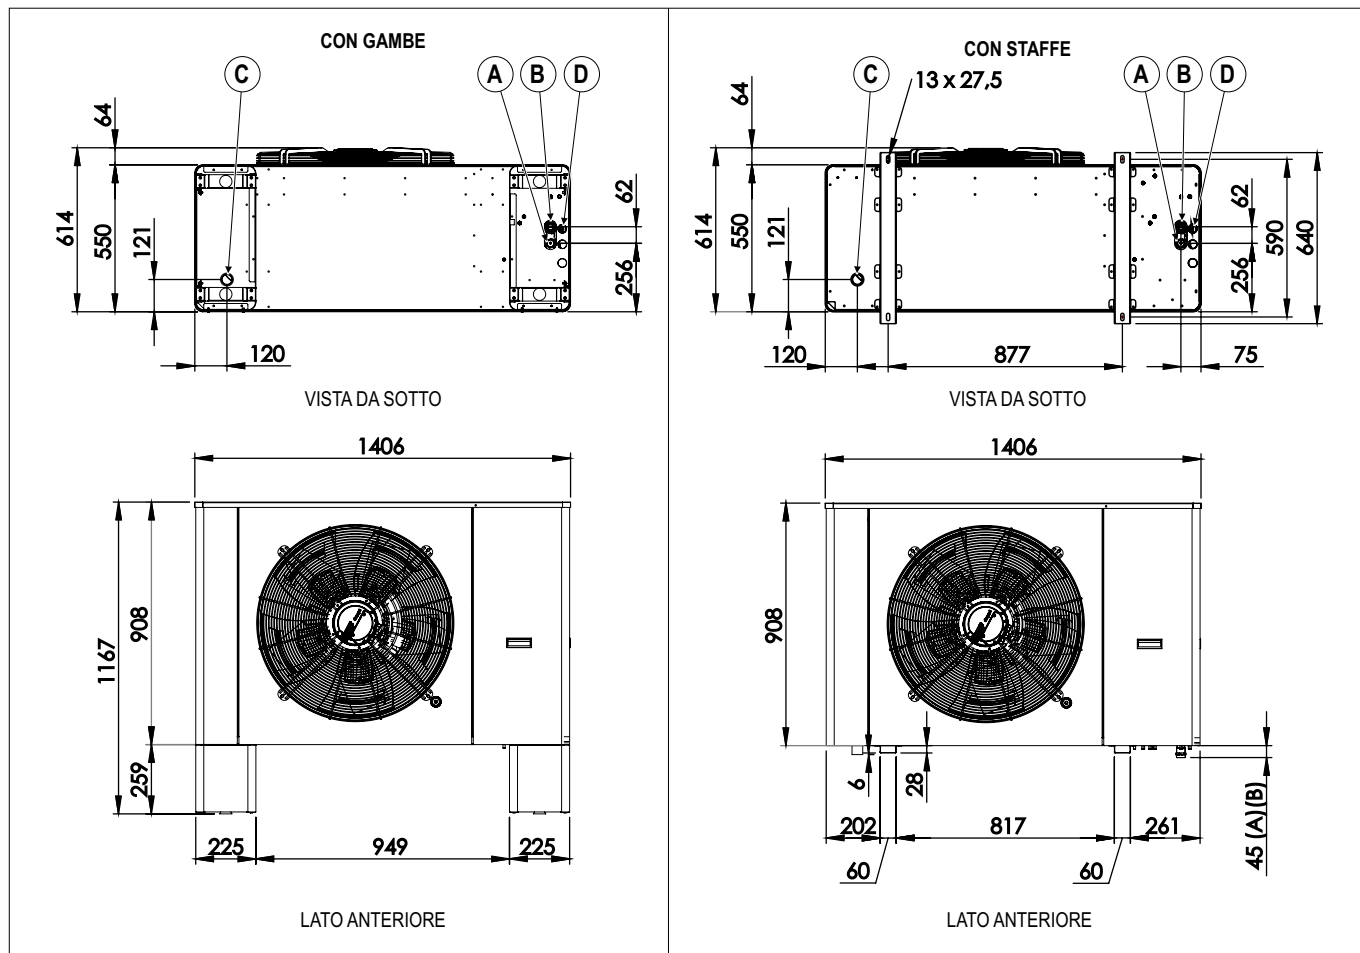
(Dimensioni Serie S - SP - SP-T - con gambe e con staffe)
